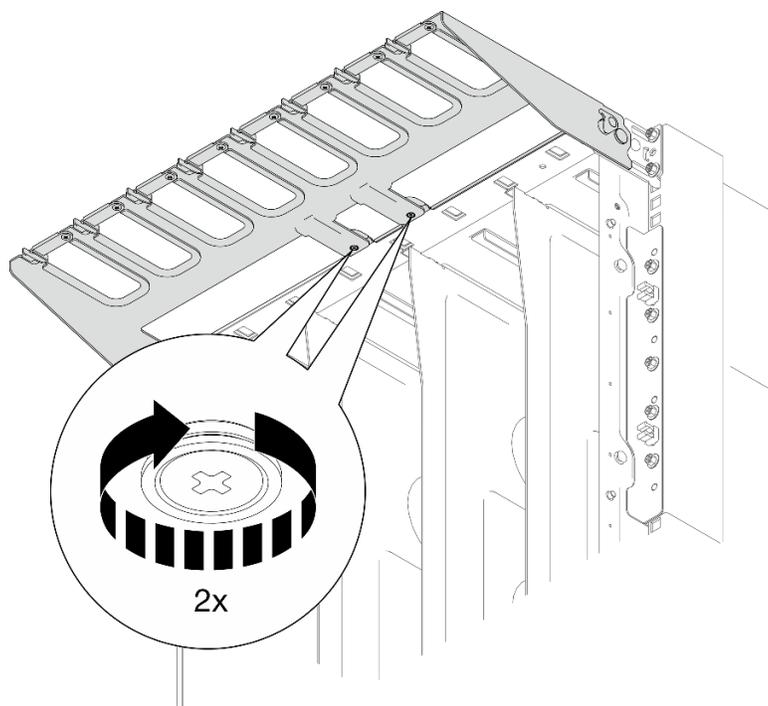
Installation de deux vis par le dessous du support supérieur avant.
